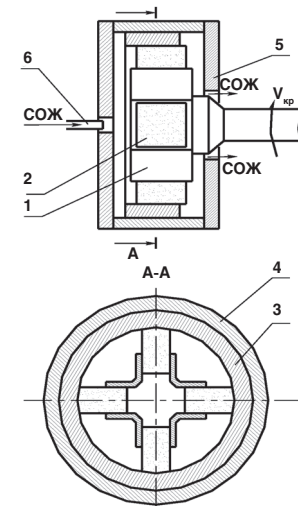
Принципиальная схема внутреннего шлифования сборными абразивными кругами с радиально подвижными сегментами: 1 — инструмент, 2 — сегменты, 3 — заготовка, 4 — емкость, 5 — крышка, 6 — трубопровод.
